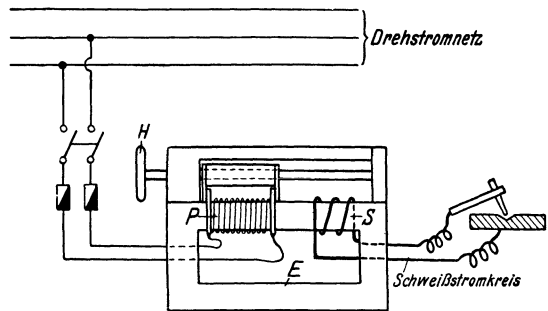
Schweißumspanner mit verschiebbarer Spule.
